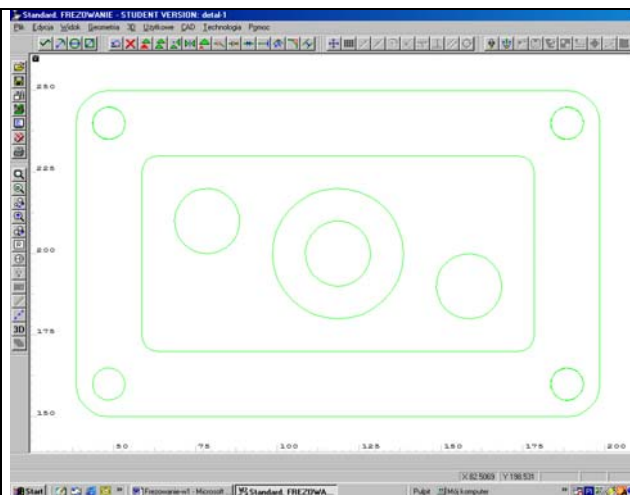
Przygotowany kontur detalu do zapisu w formacie DXF
